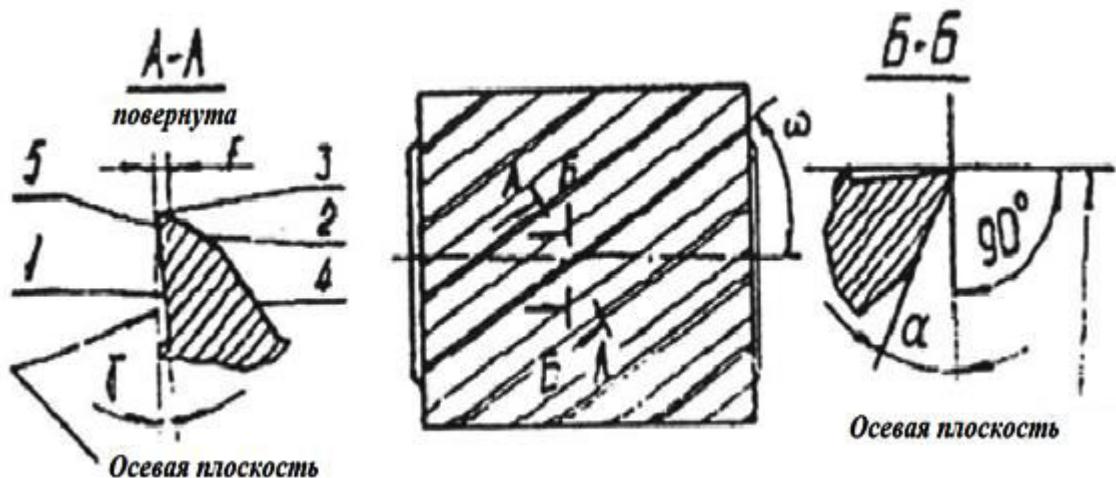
Геометрия зуба цилиндрической фрезы:
